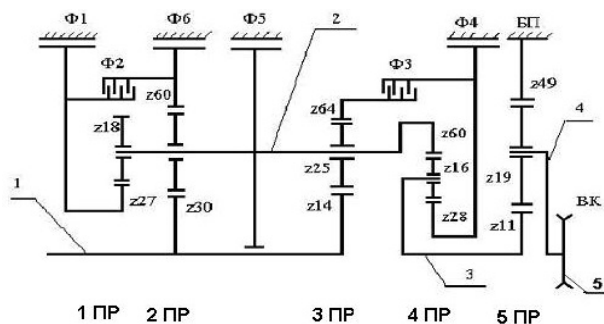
Кинематическая схема бортовой коробки передач танка Т-64Б
